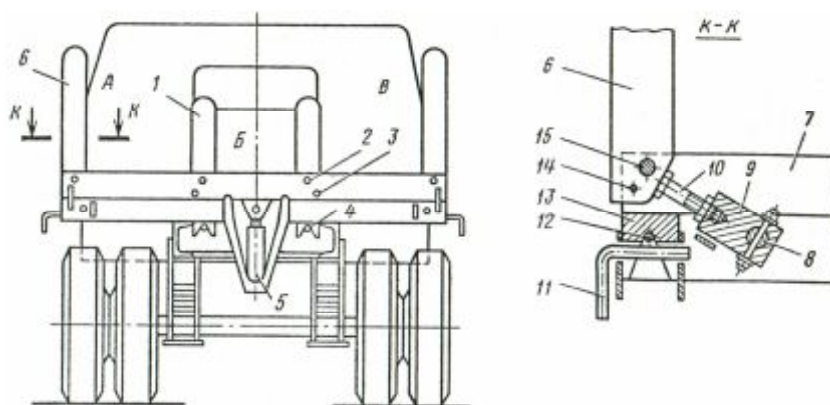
Самосвальный коник для перевозки трех партий металла
